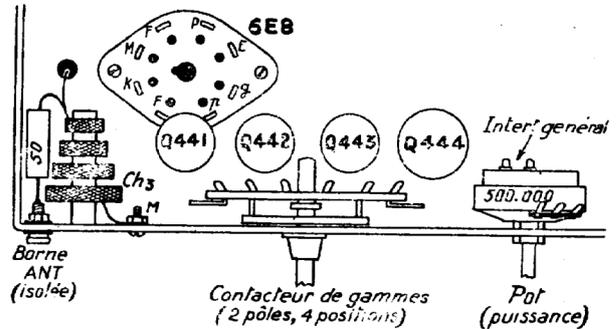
Montage des bobinages pour la récepteur à plusieurs gammes O. C.
